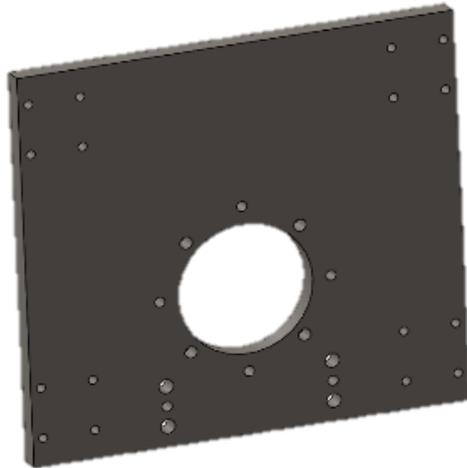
Diseño 3D de la placa de soporte del motor y caja de rodamientos.
